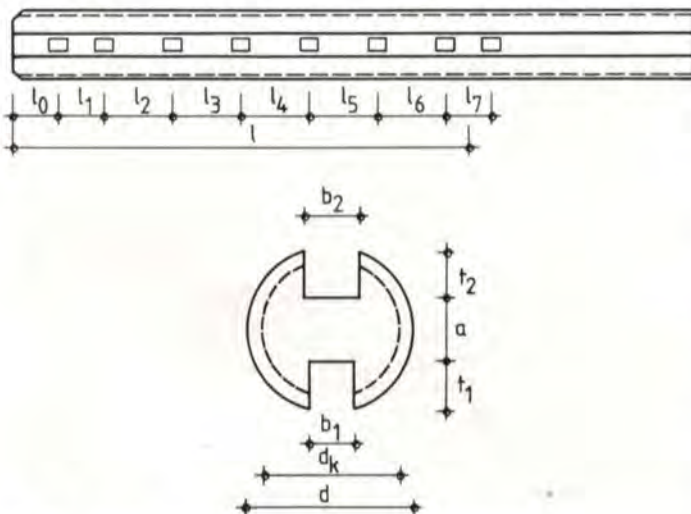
Quer- und Längsschnitt durch eine Gewindestange
